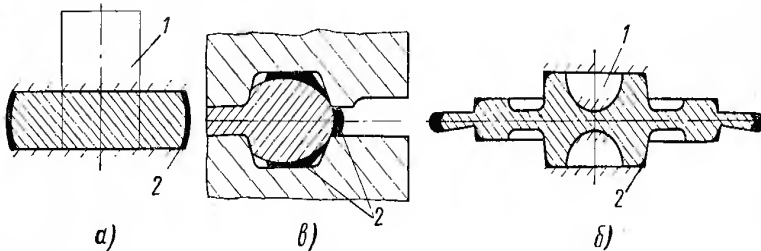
Схема распределения стекла в поковках: *а* – на заготовке после осадки; *б* – в поковке шестерни; *в* – на ободе в процессе штамповки; 1 – пленка стекла; 2 – скопление стекла
